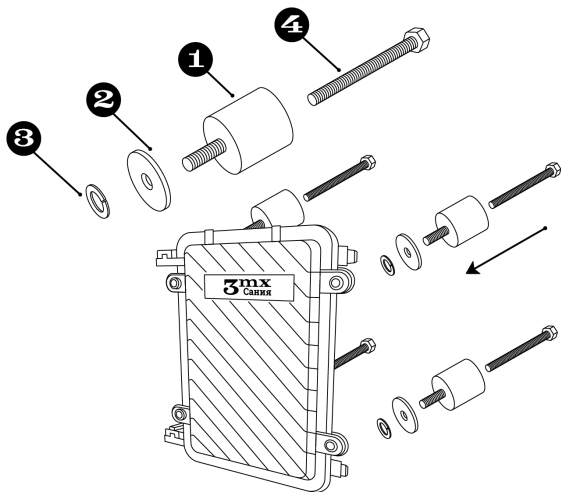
Комплектующие для сборки соединительного крепления детектора
